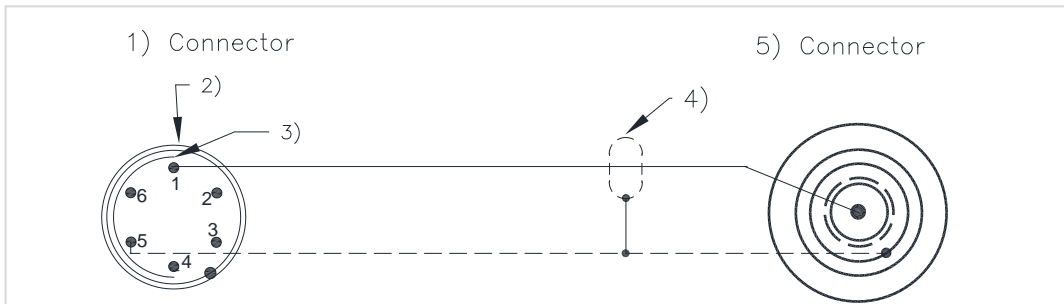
Anschlüsse Kabel - Blick auf die Steckseite / Connection Cable - View on connection / Câble - Vue de côté de Connexion
